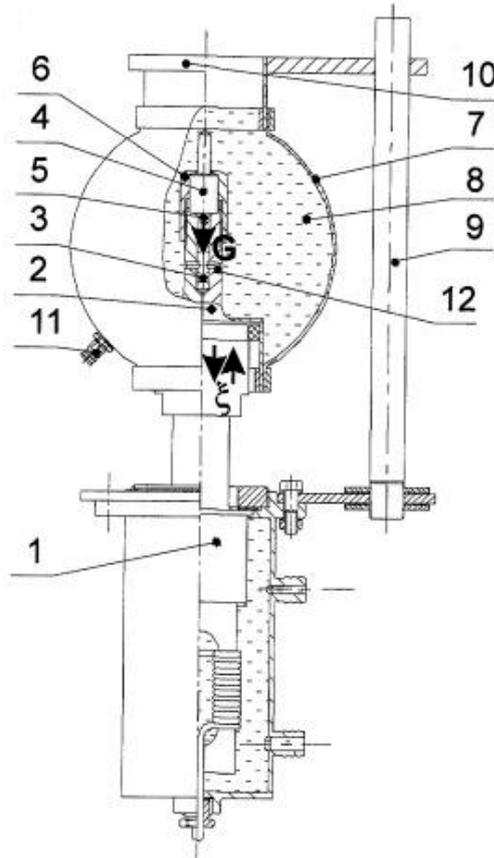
Патент RU 2354525. Устройство для разборки распылителей форсунок: 1- источник ультразвуковых колебаний, 2- конденсатор; 3- осевой канал; 4- корпус распылителя; 5- игла распылителя; 6- упор; 7- камера для моющего раствора; 8- моющий раствор; 9-траверса; 10- кронштейн; 11- заливной штуцер; 12 –сквозное отверстие
